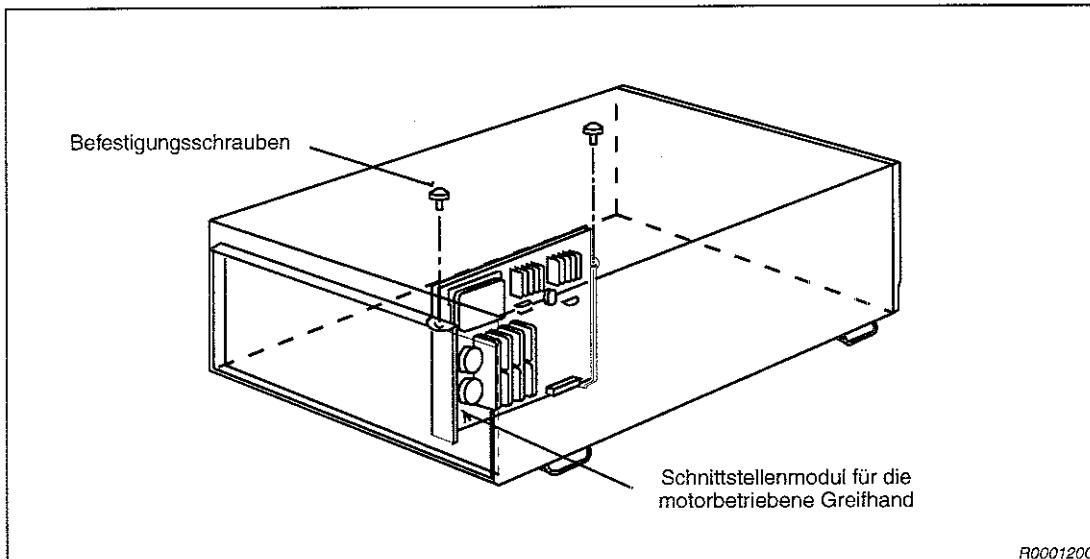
Einbau des Steuermoduls für die motorbetriebene Greifhand
